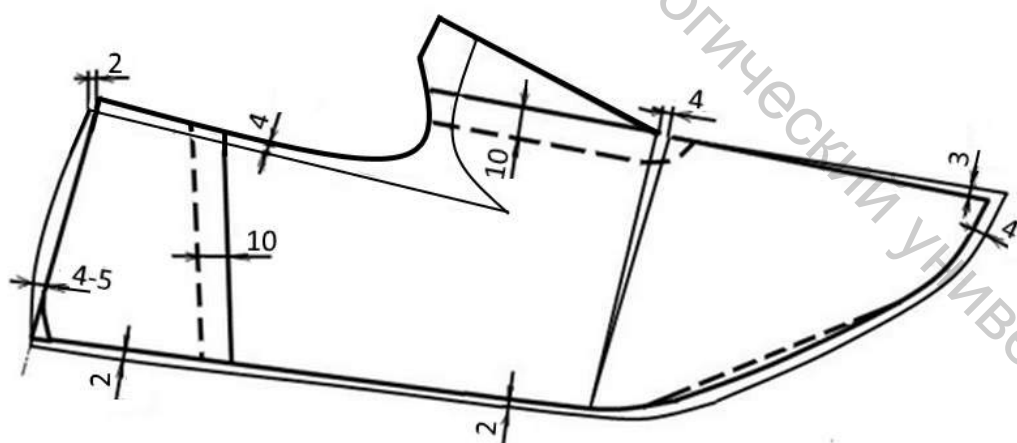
Построение подкладки для полуботинок без специального крепления
